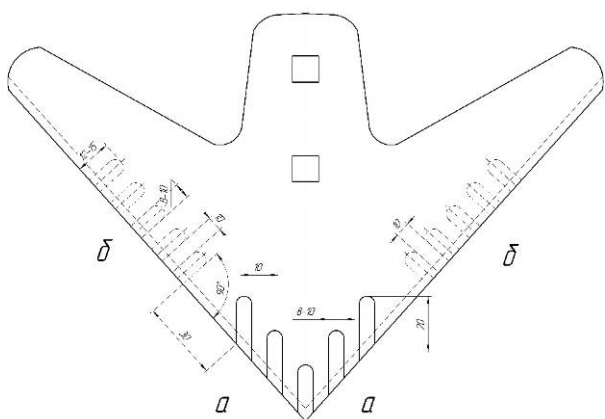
Схема наплавки упрочняющих полос на поверхность стрелчатой лапы культиватора: а – носка; б – крыльев
